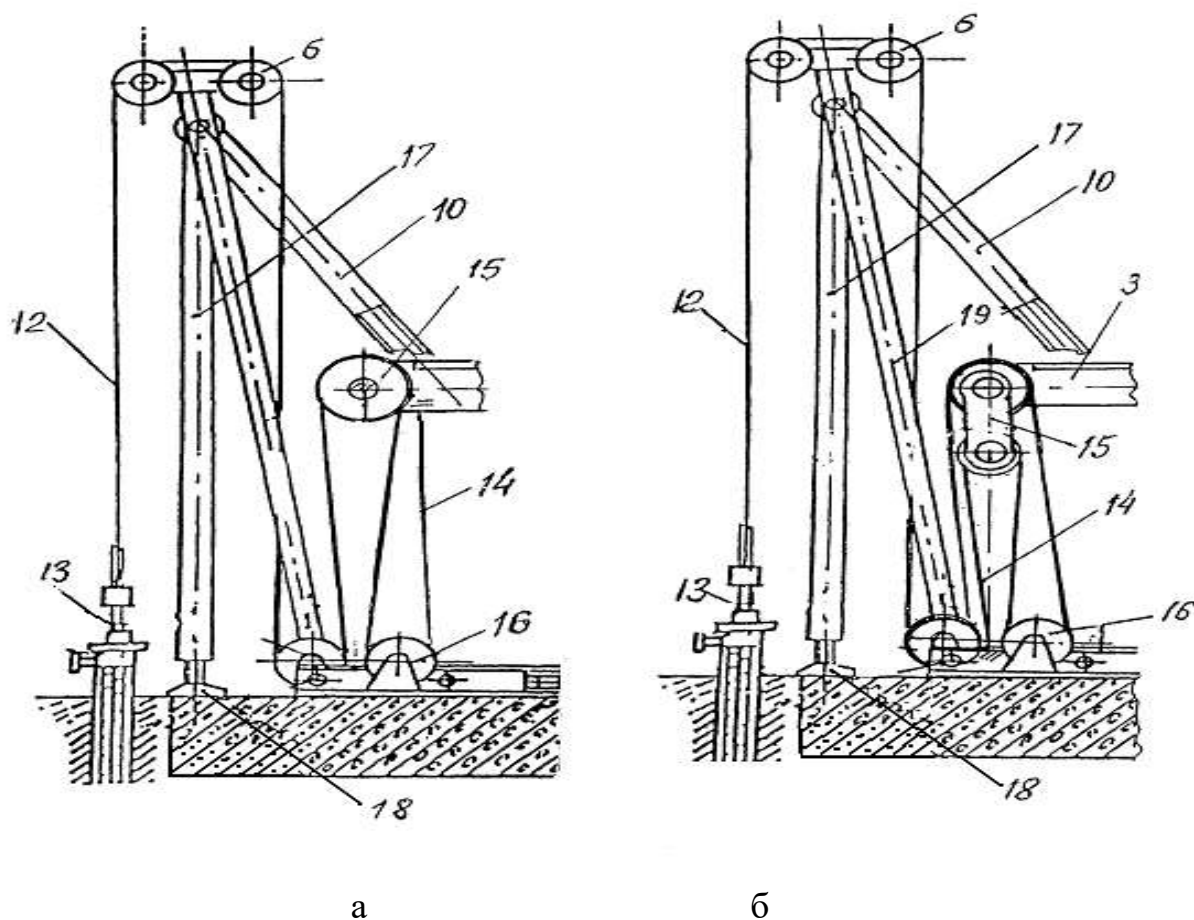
Балансирный привод штанговой насосной установки
